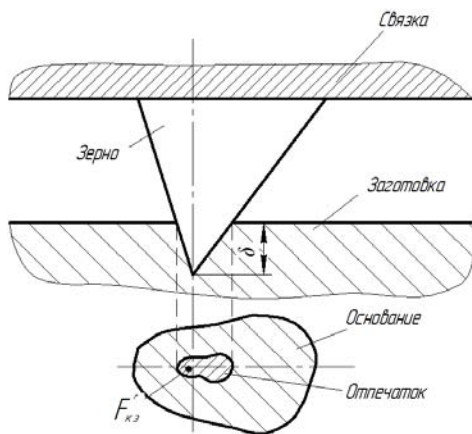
Геометрическая схема внедрения конического зерна в пластичную поверхность
